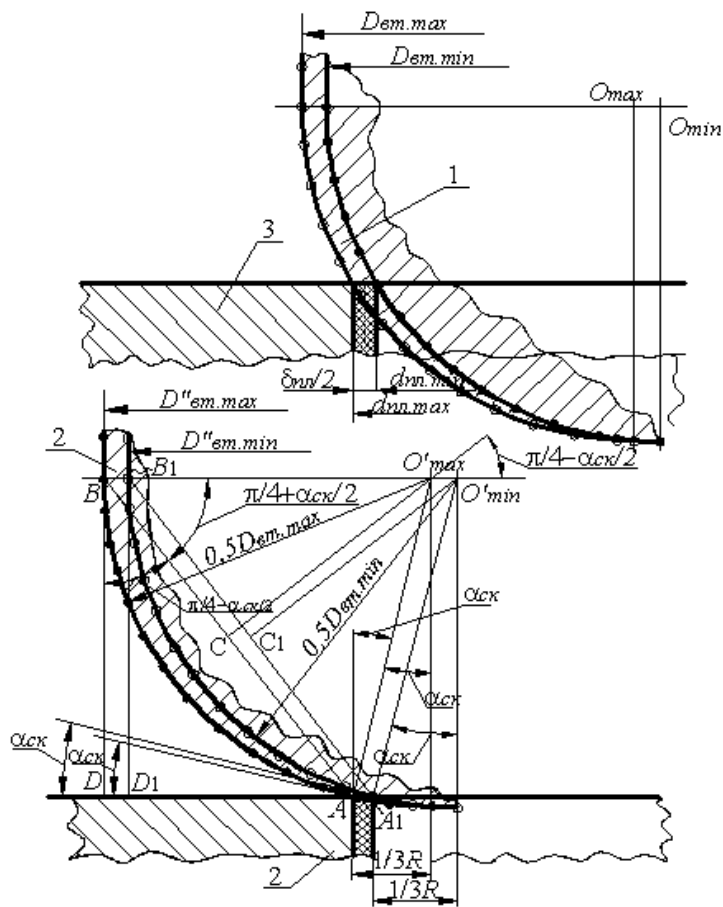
Розрахункова схема для визначення величини розкриття стикового шва згортної втулки із округленням: 1 – положення згортної втулки з закритим стиковим швом перед її запресуванням у отвір пластини; 2 – положення згортної втулки з максимально допустимим розкритим стиковим швом перед її запресуванням у отвір пластини; 3 – внутрішня пластина
